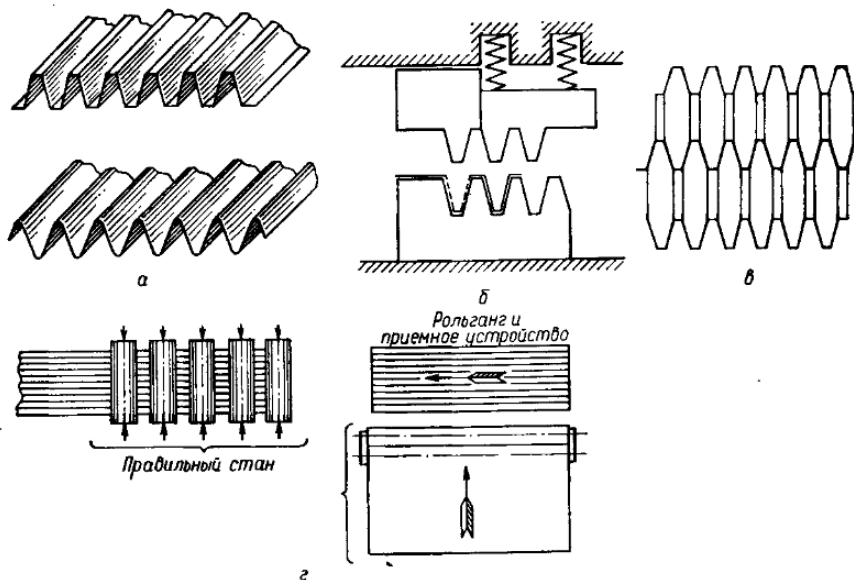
Схема технологічного процесу отримання гофрового заповнювача: а – типи гофри; б - штампування гофри; в - прокатка гофри; г - схема установки для отримання гофри
